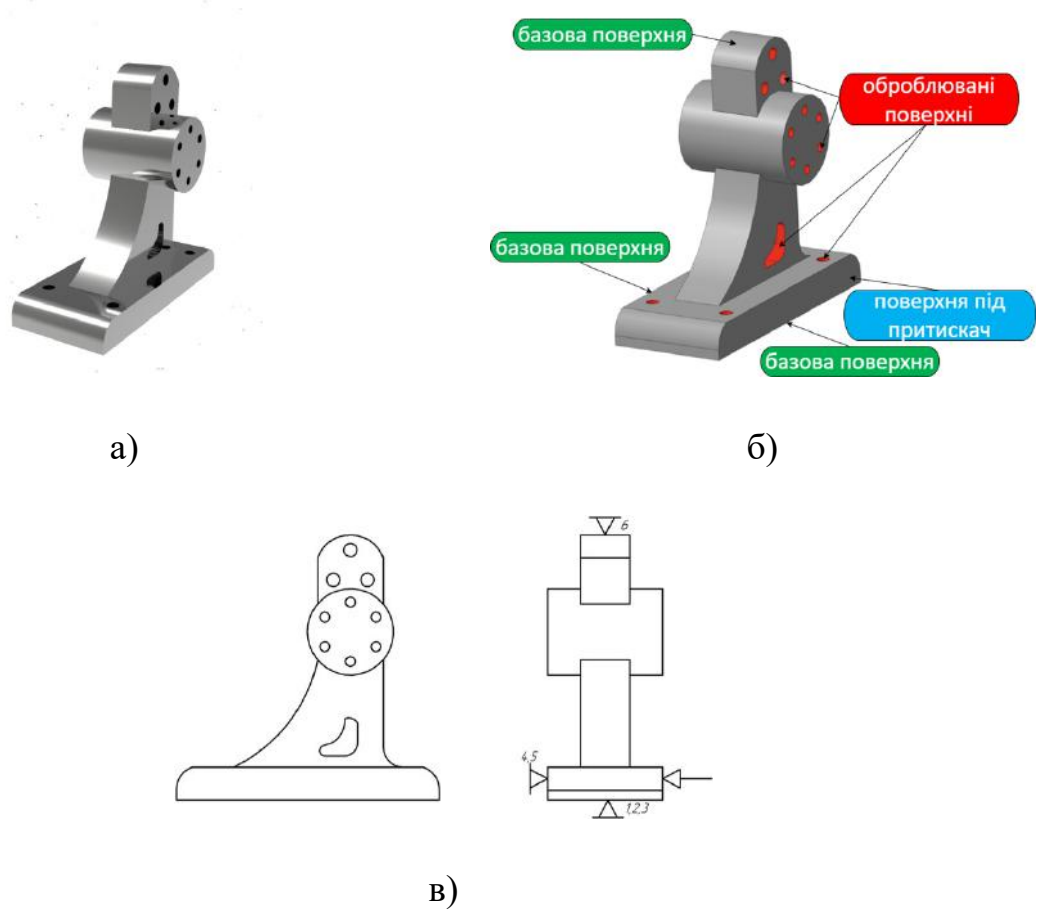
Деталь типу кронштейни: а – загальний вигляд;
